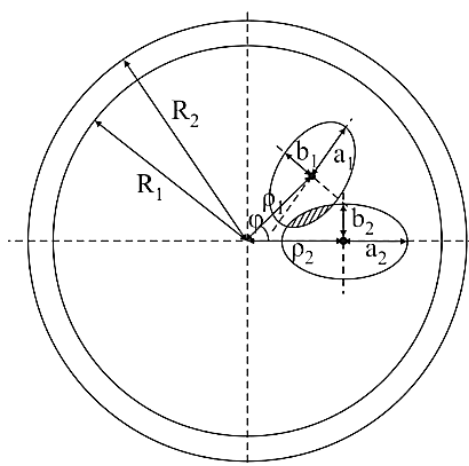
Схема перекрытия отверстий овальной формы в упругих пластинах универсального поворотного компенсатора
